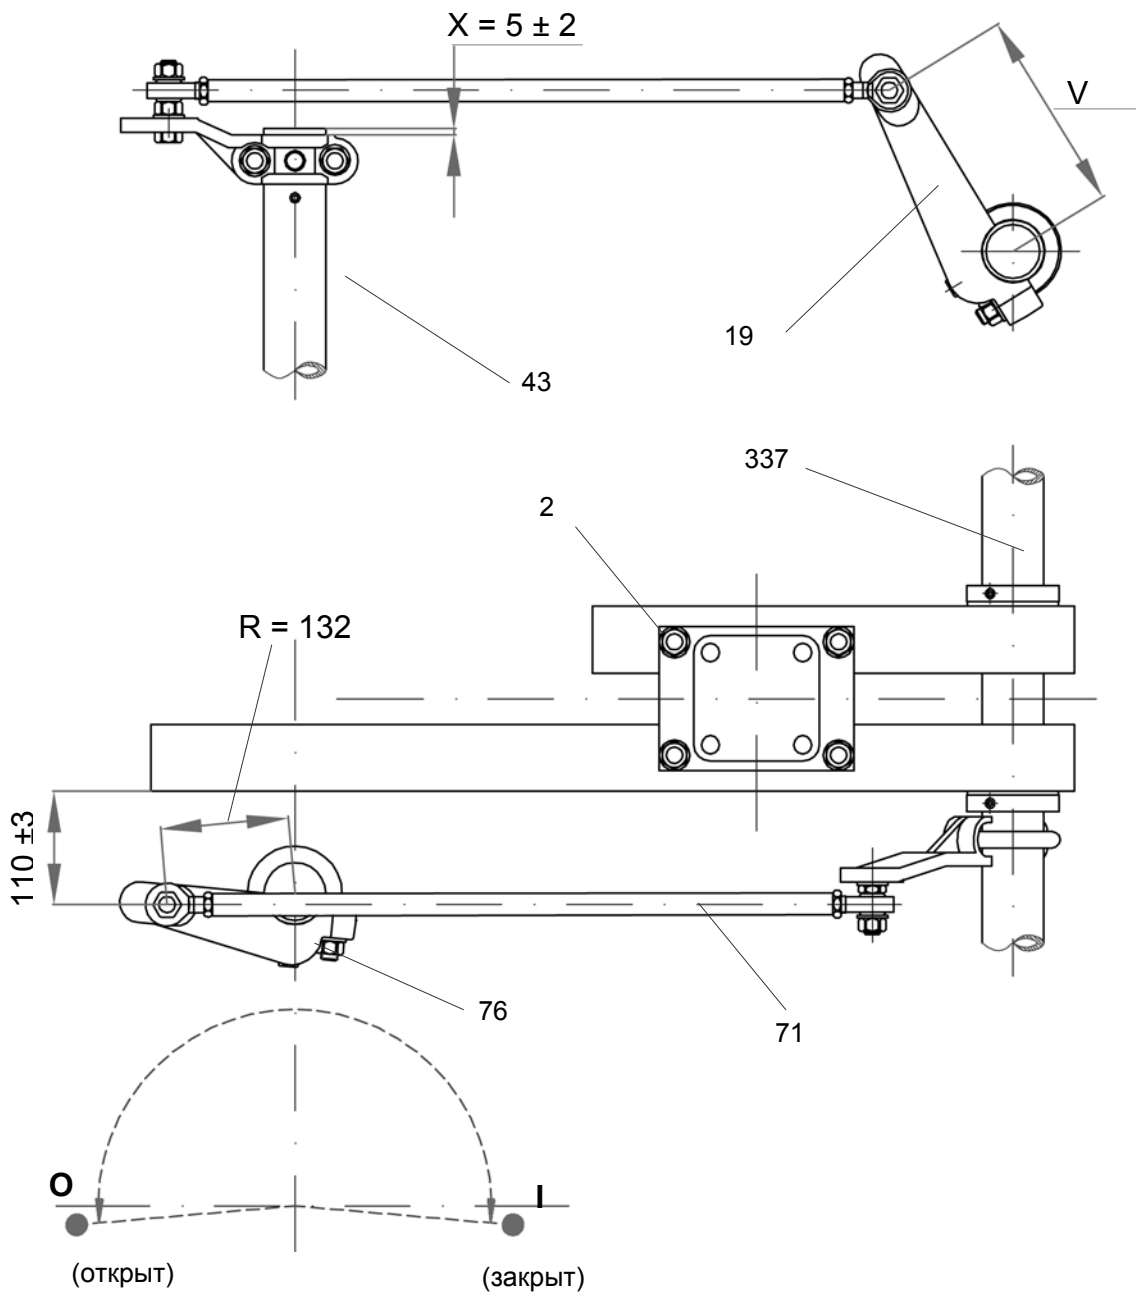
Крепление приводного механизма заземлителя – опосредованный монтаж размер $m3$
